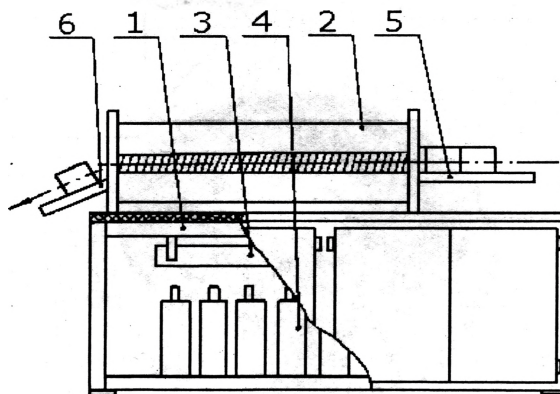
Схема кузнечного индукционного нагревателя типа КИН 500 конструкции МАЗ: 1 — каркас, 2 — индуктор, 3 — медная шина, 4 — конденсаторная батарея, 5 — механизм загрузки, 6 — лоток выгрузки
